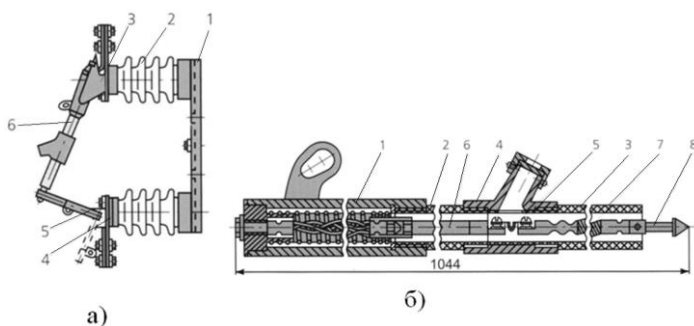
Предохранитель ПВТ-35: а – общий вид: 1 – основание; 2 – опорный изолятор; 3 – верхняя головка; 4 – нижняя головка; 5 – контактный нож; 6 – патрон. б – патрон: 1 – корпус; 2, 3 – винипластовые трубки; 4 – стальной патрубок; 5 – плавкая вставка; 6 – токоведущий стержень; 7 – гибкий проводник; 8 – наконечник
